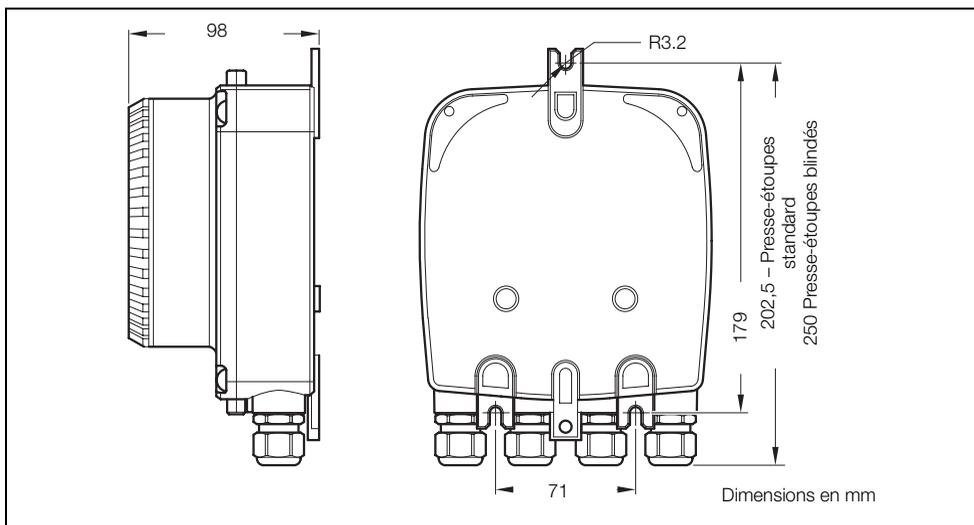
Dimensions du transmetteur déporté (Presse-étoupes standard montés)
